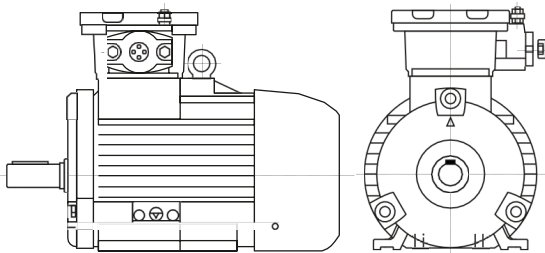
Пример конструктивного исполнения электродвигателя ВА80
